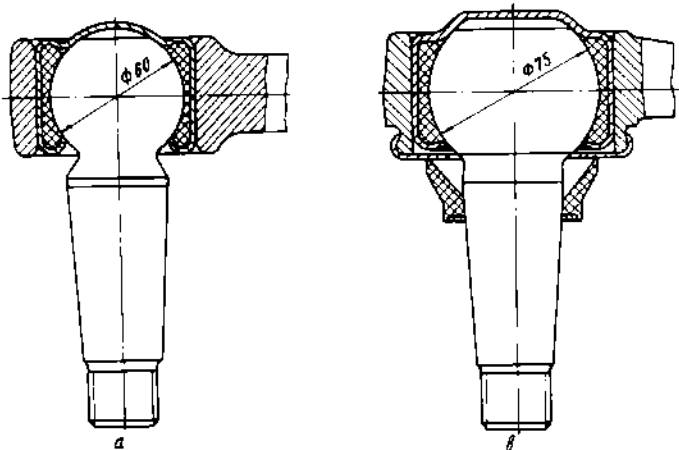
Реактивная штанга задней подвески с шарнирами:
